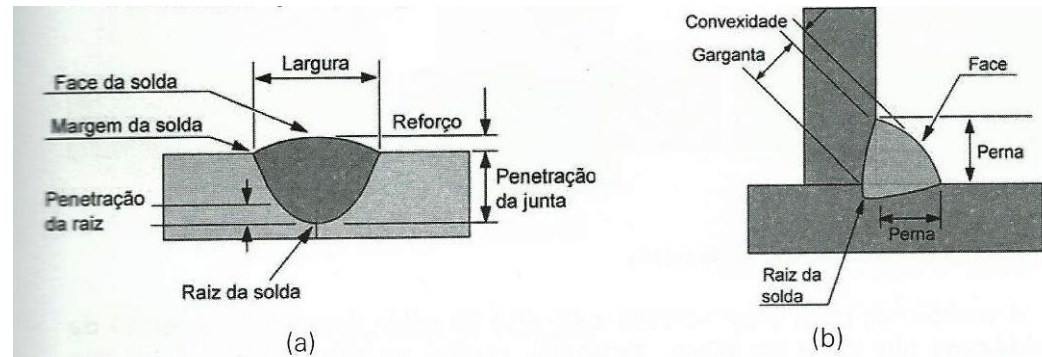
Dimensões e regiões de soldas de topo (a) e de filete (b)
